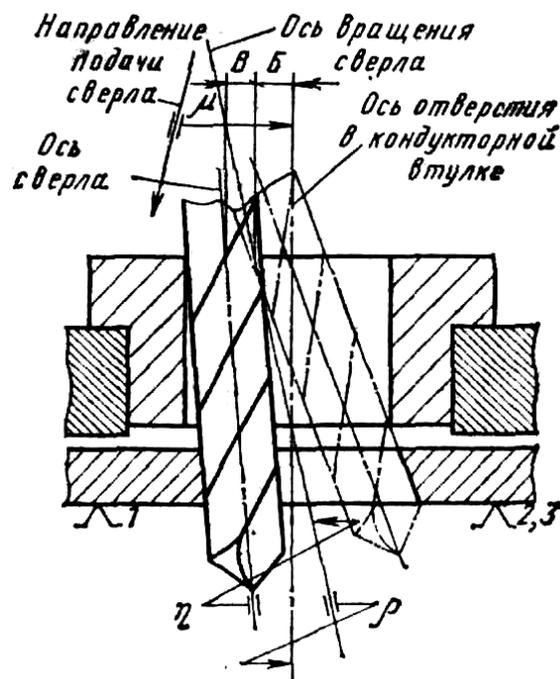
Схема отклонений положения и направления подачи сверла относительно отверстия в кондукторной втулке
